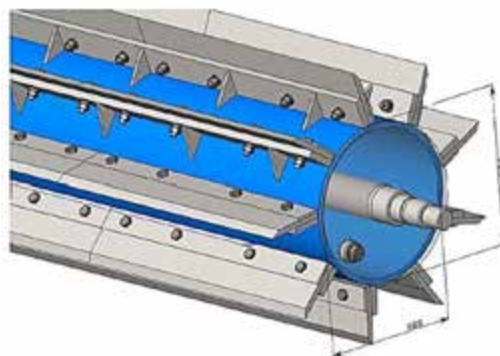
Конструктивна схема типового катка-подрібнювача барабанного типу
